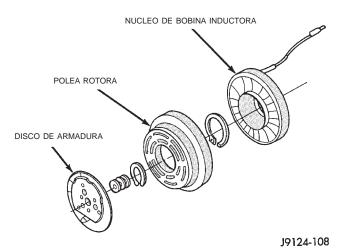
Disco de embrague/polea/bobina inductora INSPECCION
